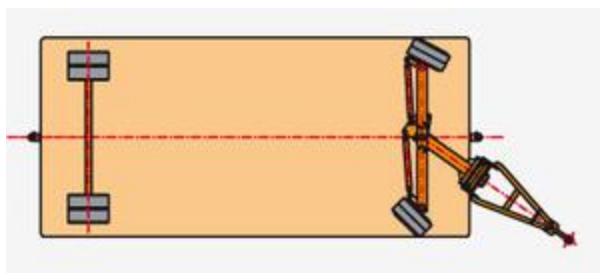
Грузовые тележки с поворотными колесами
